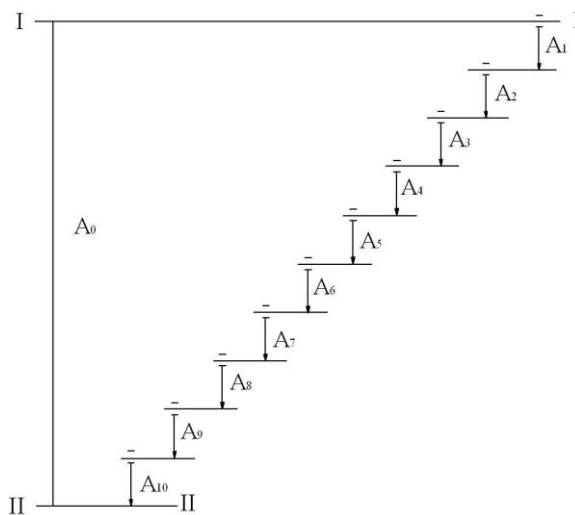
Размерная цепь смещения осей зубчатой пары машины шлифовальной угловой
